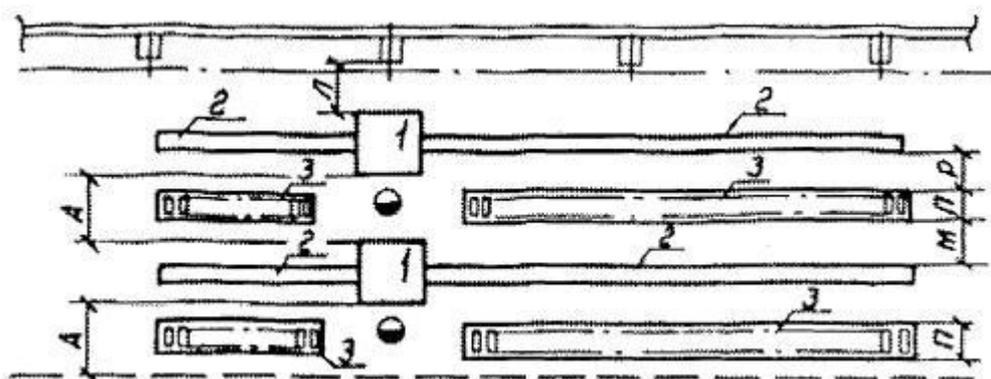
Размещение оборудования для сварки длинномерных деталей:
